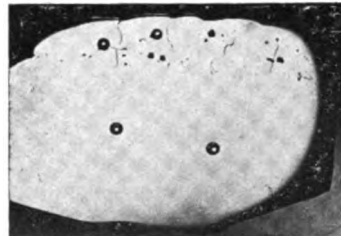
Ungeätzt, Lichtbogenschweißung mit Schweißdraht von 0,1 v. H. C-Gehalt, nat. Größe.
